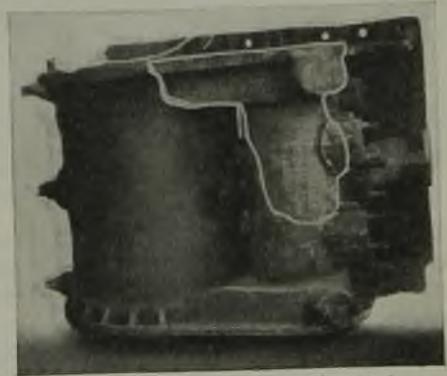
b. Lokomotivzylinder nach der Schweißung.
